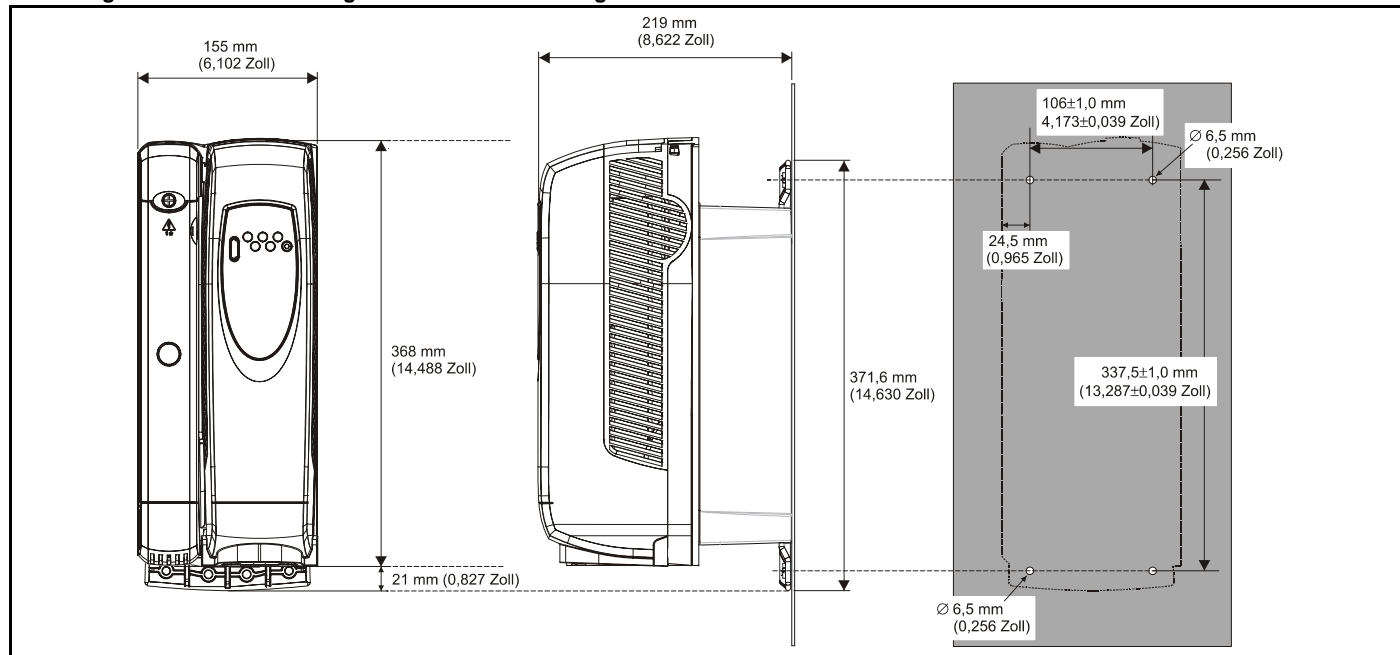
Rückwandmontage für Umrichter der Baugröße 3
